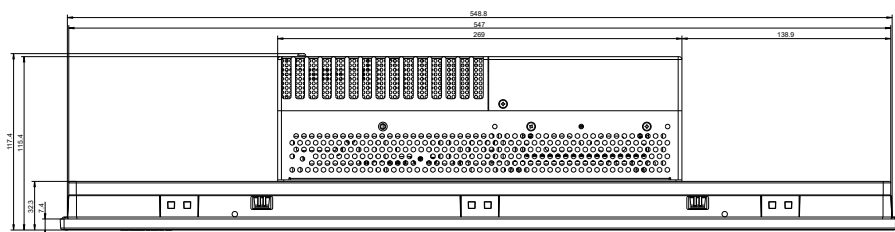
Размеры корпуса устройства VR4x21, вид сверху
